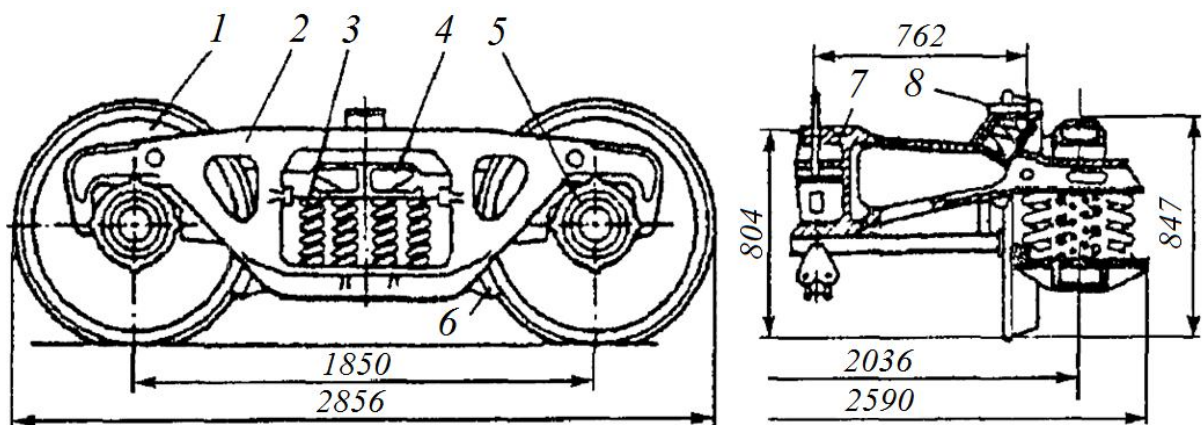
Тележка модели 18-115: 1 – колесная пара; 2 – боковая рама; 3 – рессорный комплект; 4 – надрессорная балка; 5 – буксовый узел; 6 – тормозная колодка; 7 – плоскость подпятника; 8 – упруго-фрикционный скользящий
